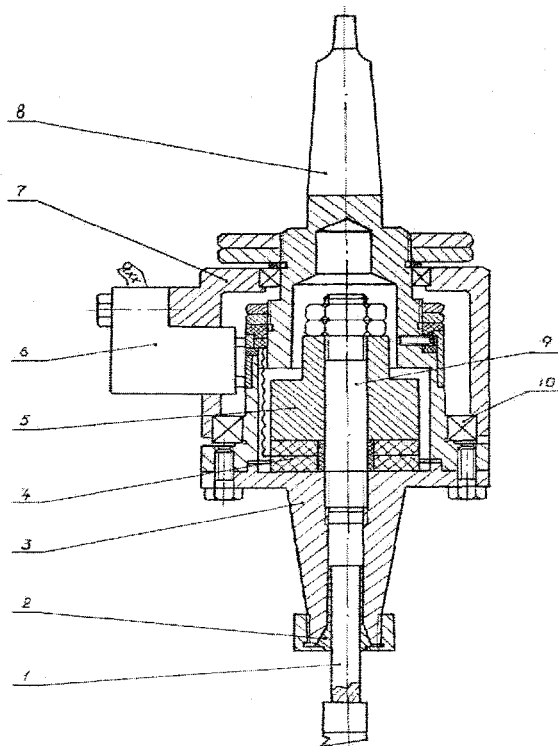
Ультразвуковое устройство для нарезания резьбы резцом
